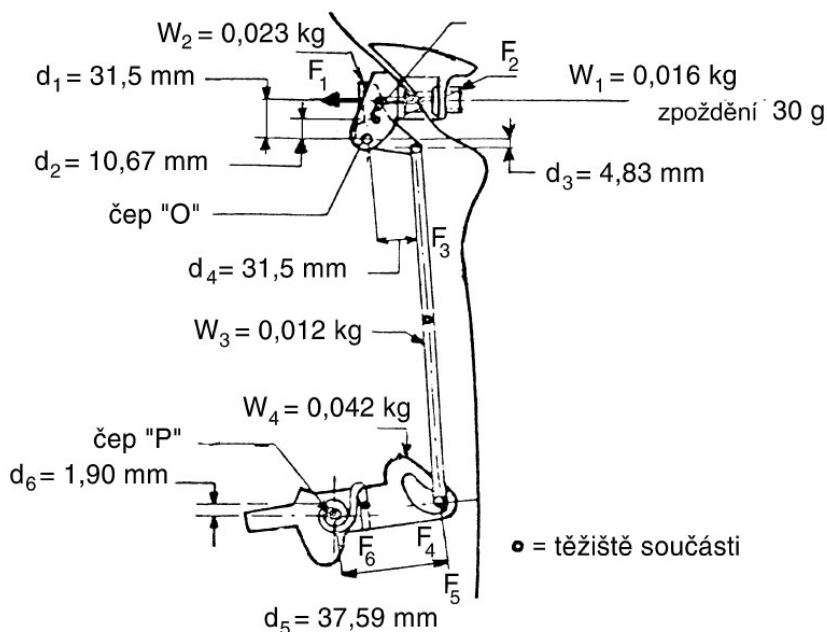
Zámek dveří - zařízení pro zkoušku statickou podélnou silou [28]
